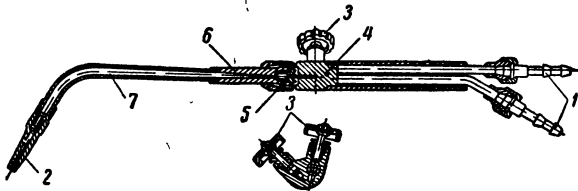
Ацетилено-кислородная сварочная горелка типа СУ-48:
